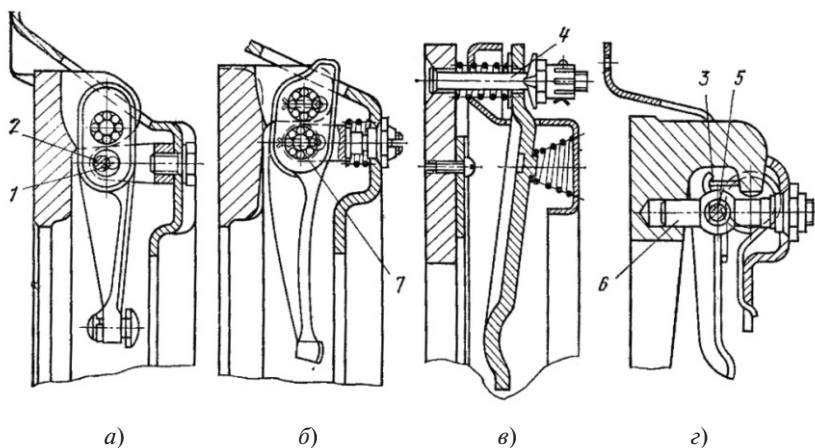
Конструктивные схемы рычагов выключения сцепления
